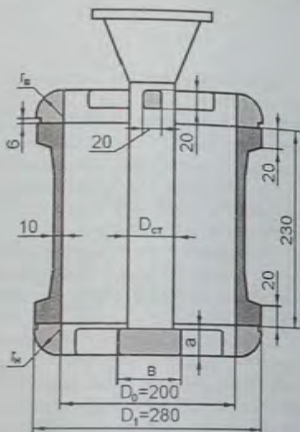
Схема модельного блока для отливки "Полый цилиндр"
